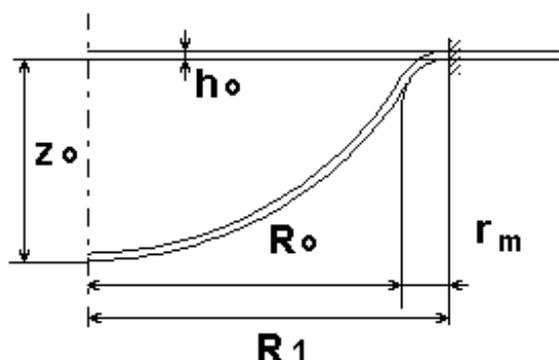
Расчетная схема формоизменения осесимметричной тонколистовой заготовки
